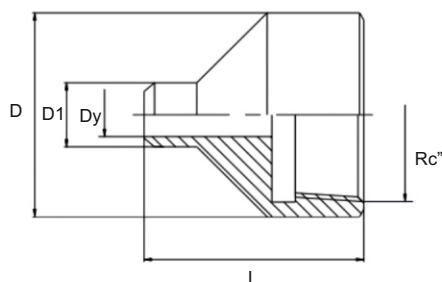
Муфта переходная для соединения РВД с трубопроводом
